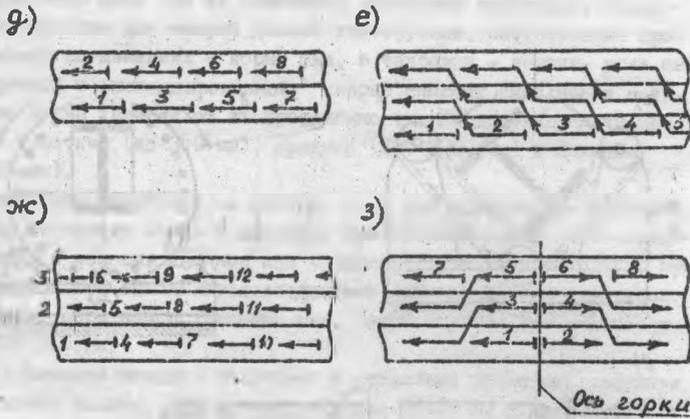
Способы сварки швов: а - сварка "напроход"; б - сварка от середины к краям; в - обратно-ступенчатый способ; г - обратно-ступенчатый способ от середины к краям; д - сварка двойным слоем; е, з - сварка каскадом и горкой; ж - сварки секциями.
